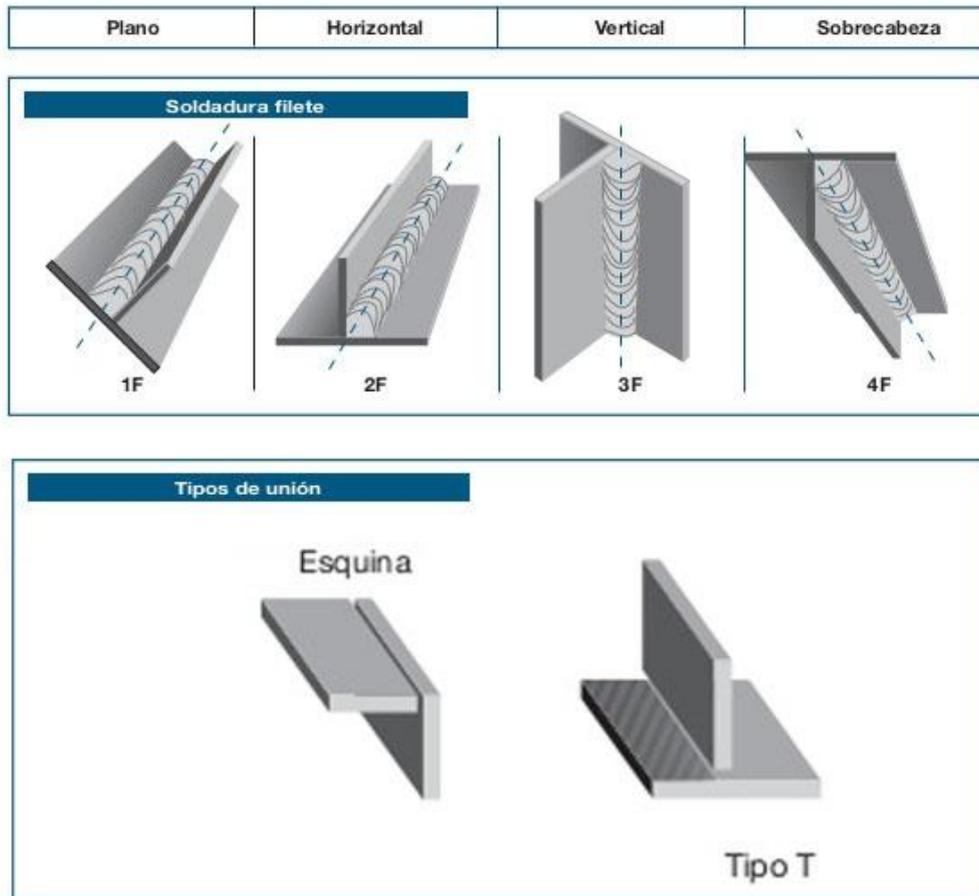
Especificaciones tipos de soldadura presentes en el proyecto.
